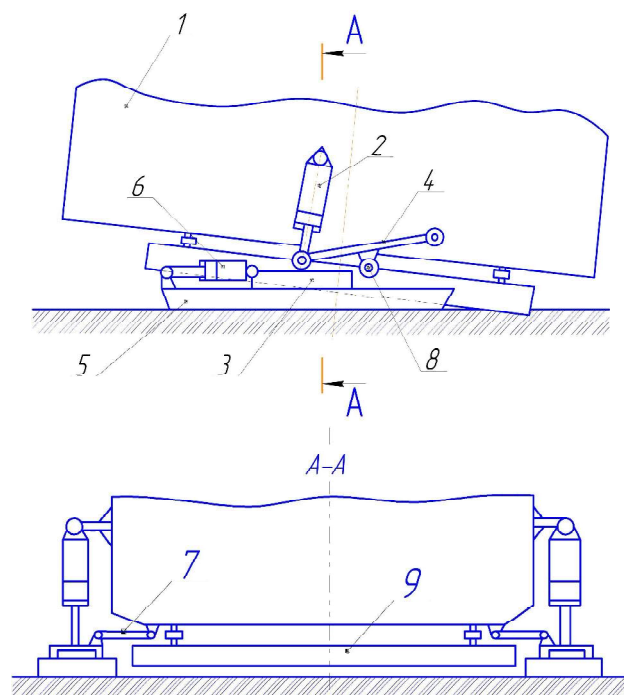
Схема трехопорного механизма шагания с неполным отрывом базы при шагании с гидростатическими опорами: 1 – кузов; 2 – гидроцилиндры подъема; 3 – скользящая опора; 4 – тяга; 5 – опорный башмак; 6 – тяговый гидроцилиндр; 7 – тяга; 8 – упор; 9 – база /
